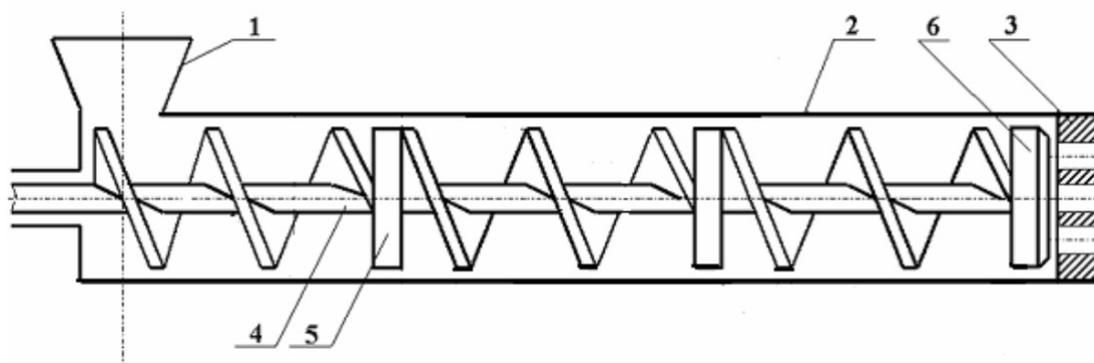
Схема прессующего механизма: 1 – загрузочное устройство; 2 – шнековый цилиндр; 3 – матрица; 4 – шнек; 5 – компрессионный затвор; 6 – головка экструдера
